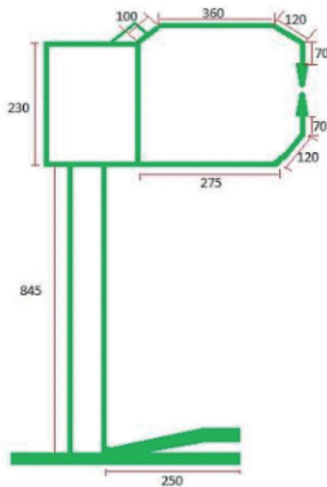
Plano con medidas de la máquina de soldadura por puntos, medidas en milímetros.
